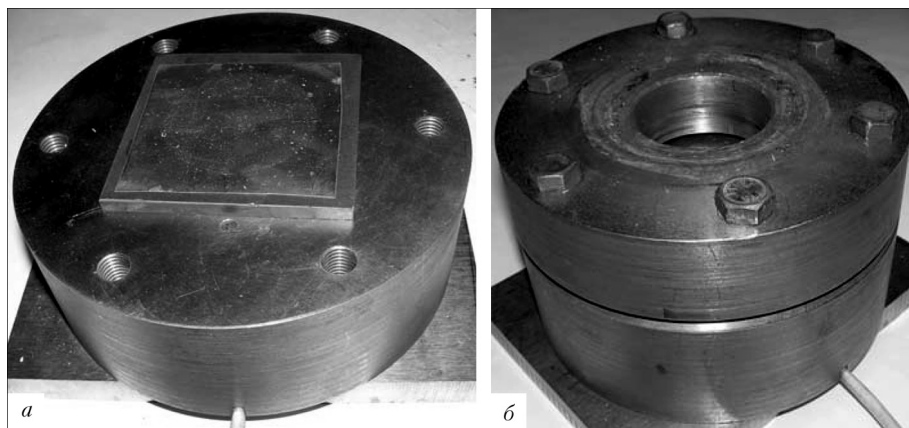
Общий вид керамической пластины, установленной на опорную плиту узла для ударного нагружения образца по схеме кругового изгиба (а) и общий вид узла в сборе (б)
